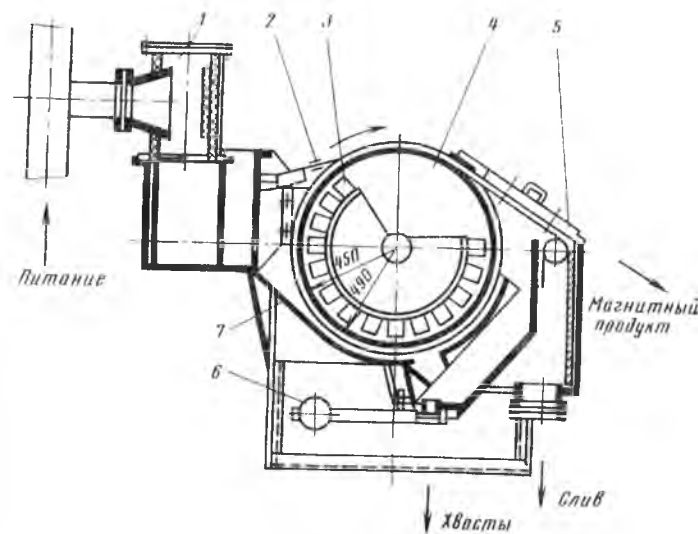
Барабанный магнитный сепаратор ПБМ-Р-90/250:
